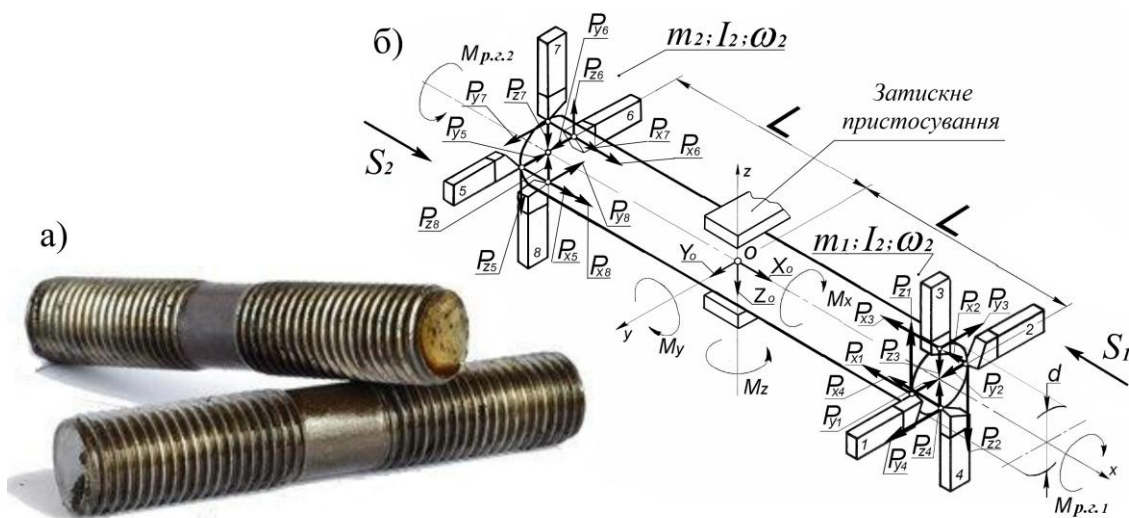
а) Загальний вигляд різьбової шпильки; б) Розрахункова схема нарізання різьби на нерухомій заготовці різьбовими головками з вісьмома ріжучими елементами.
